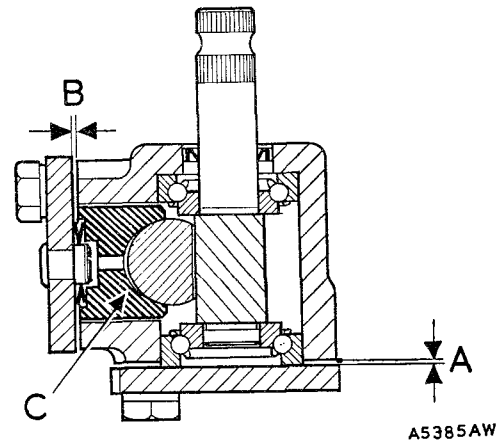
Coupe par le pignon de direction et le damper de crémaillère (1er modèle)
